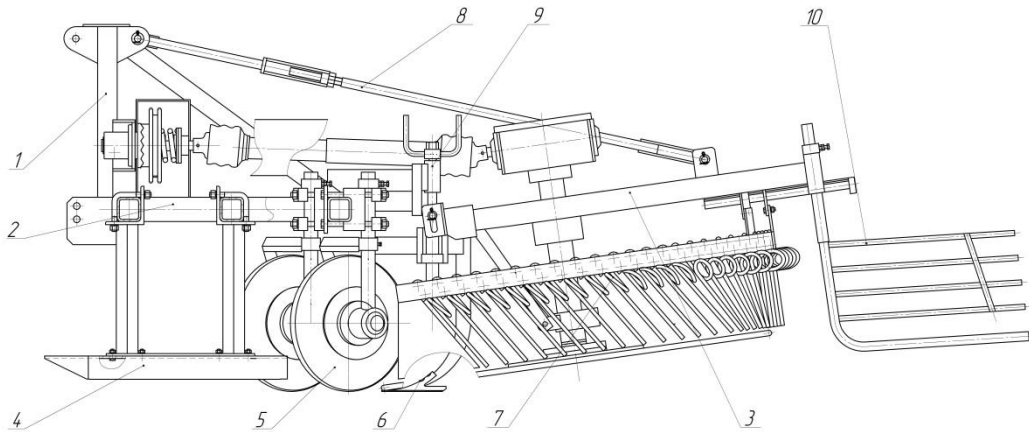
Схема копача АЗБ-6 (вид збоку): 1 – навісний пристрій; 2 – рама передня; 3 – рама задня; 4 – лижа; 5 – диск викопуючий; 6 – лапа; 7 – решітка (дека) з пружинних пальців; 8 – регулюєма тяга; 9 – гвинтовий механізм; 10 – решітка валкоутворювача
